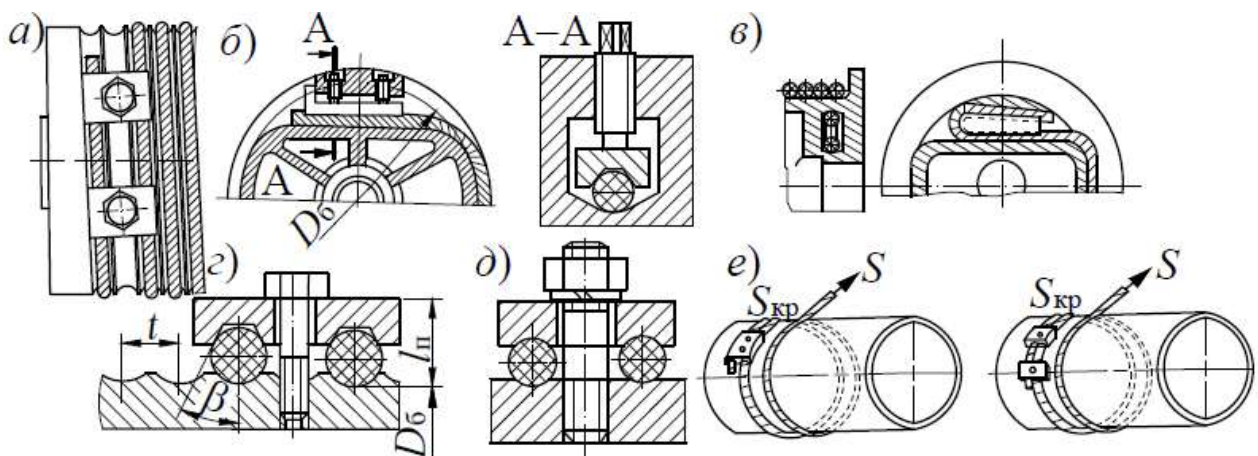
Схемы крепления каната на барабане: *а* – накладкой; *б* – прижимной планкой; *в* – клиновым зажимом; *г*, *д* – одноболтовой накладкой с трапециевидальной или полукруглой канавкой; *е* – схема крепления каната к барабану накладками
